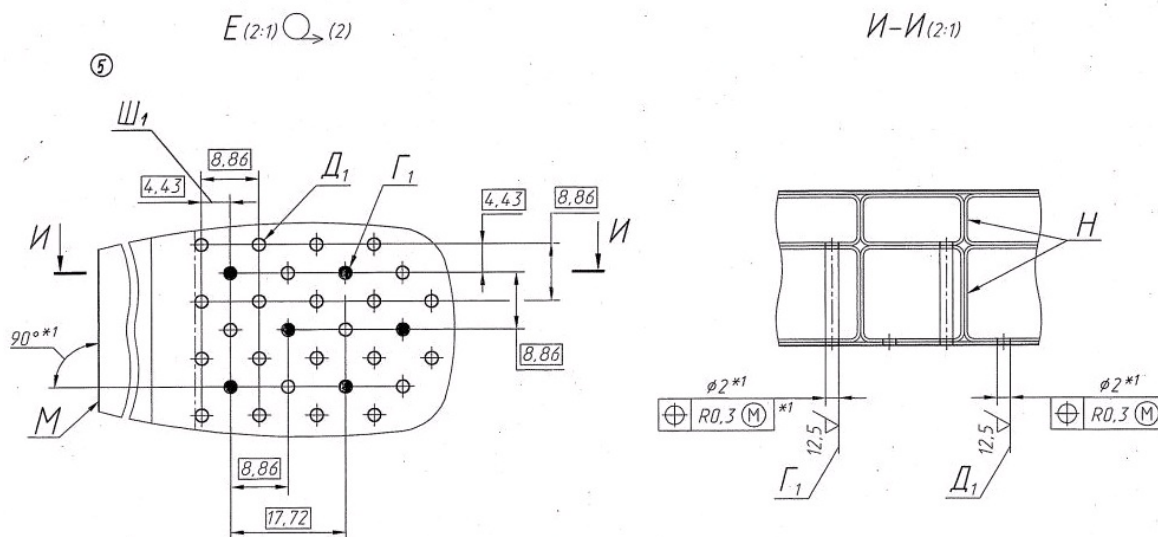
Схема расположения отверстий  $\varnothing 2$  Н16 с зависимыми позиционными допусками на сборочной единице двигателя ПС-90-А2
